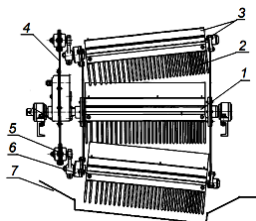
Предлагаемая конструкция очесывающего аппарата
